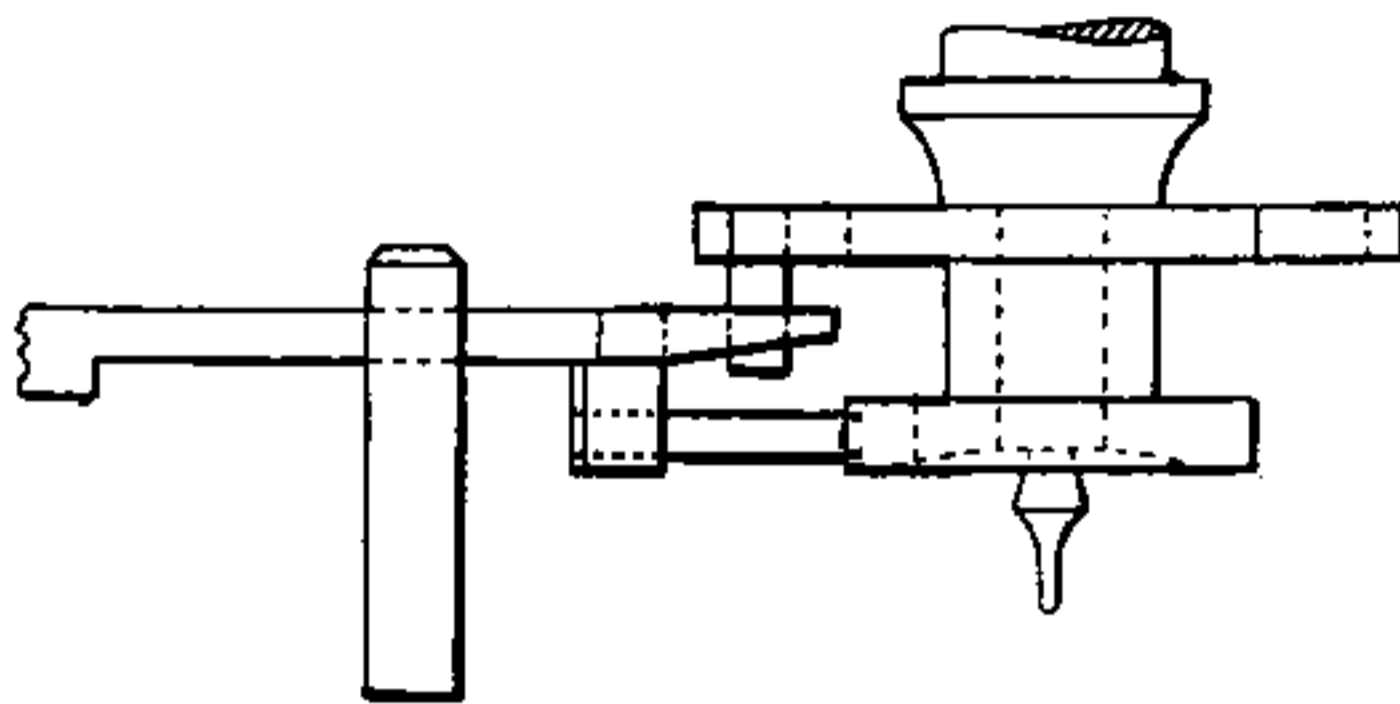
Vista ingrandita di un doppio disco e dell'estremità della forcella, illustrante la posizione corretta del dardo rispetto al piccolo disco di sicurezza.
